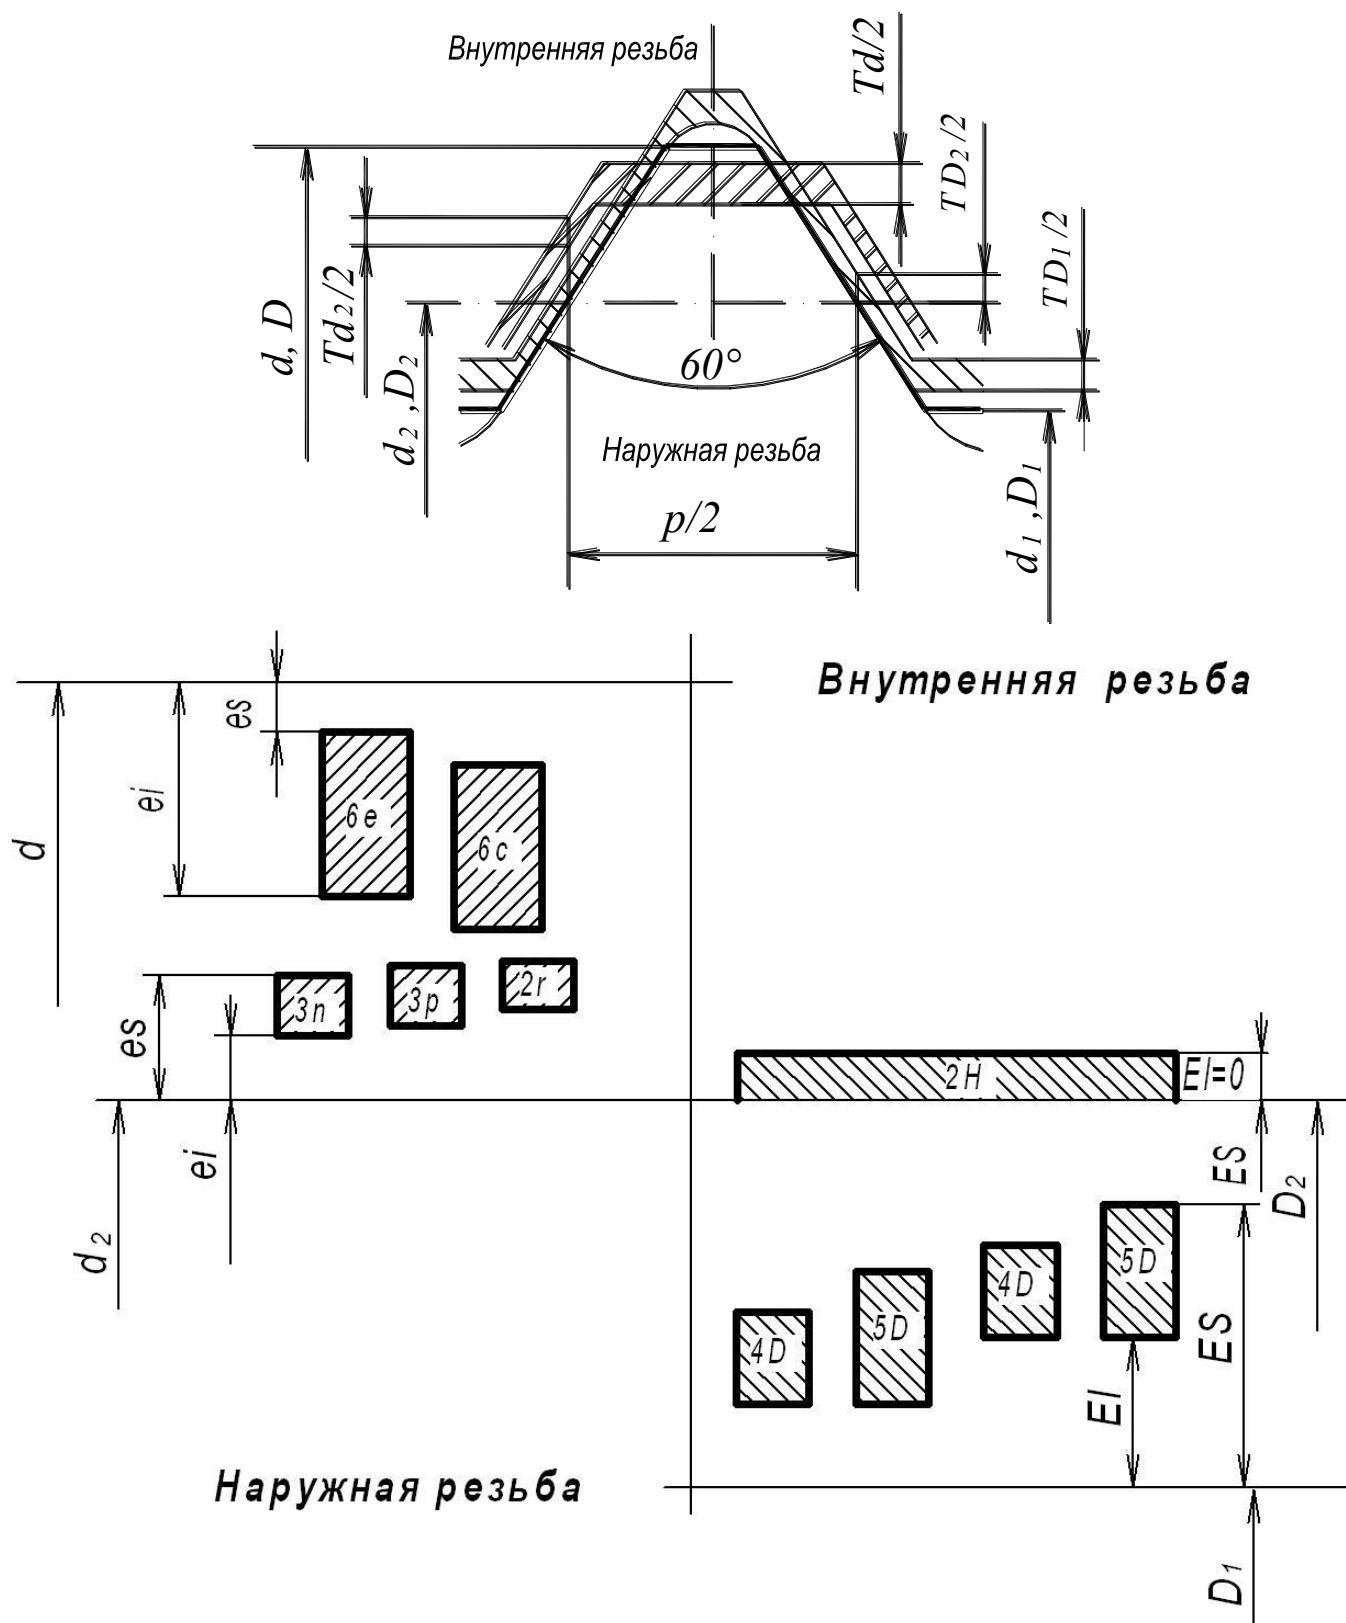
Расположение полей допусков резьбовых деталей, образующих посадки с натягом
